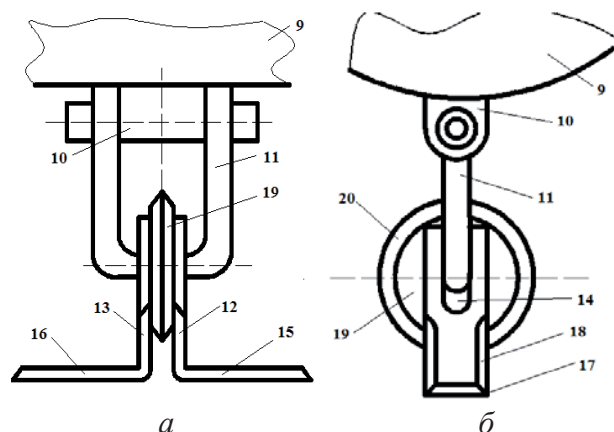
Конструктивная схема ножей-измельчителей: а – вид спереди; б – вид сбоку
